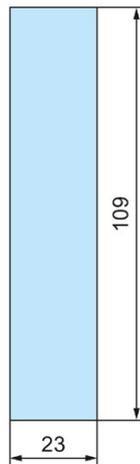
Croquis acotado de las tiras rotulables para módulos de 35 mm
